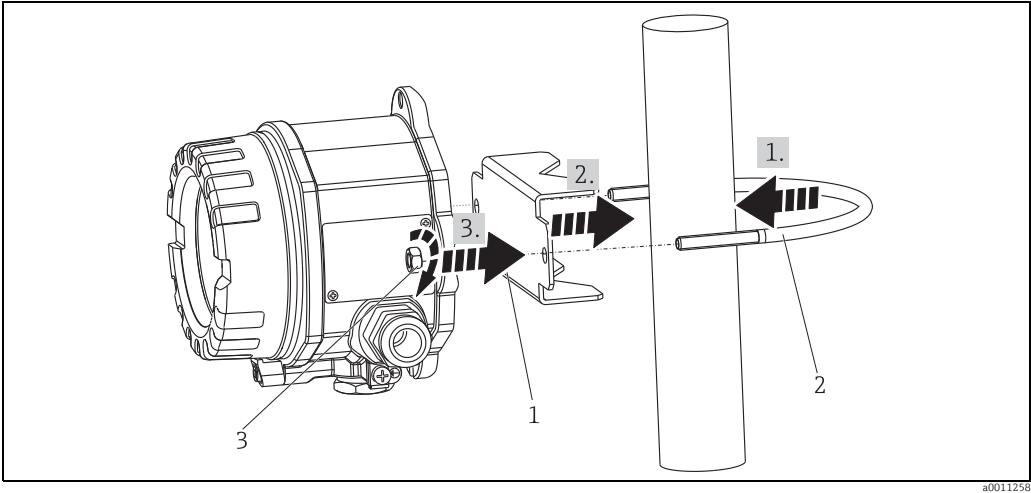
Rohrmontage des Feldanzeigers mit Montagehalter für Rohrdurchmesser 1,5...2,2 in
